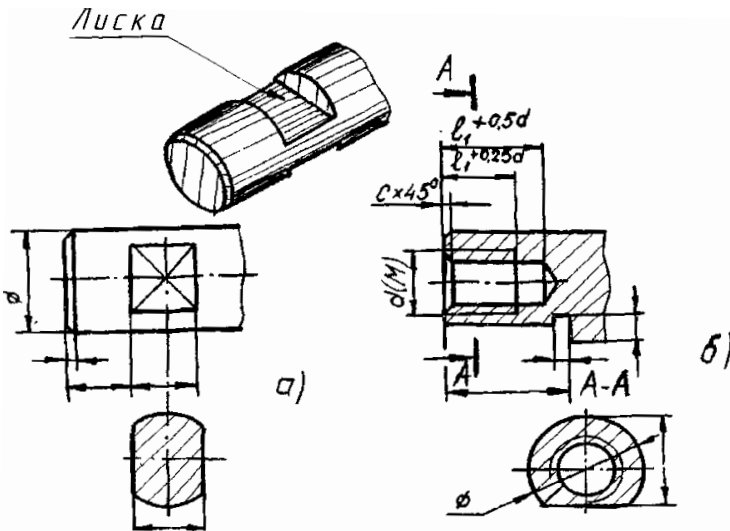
Приклади виконання креслень фрагмента деталей з лисками
